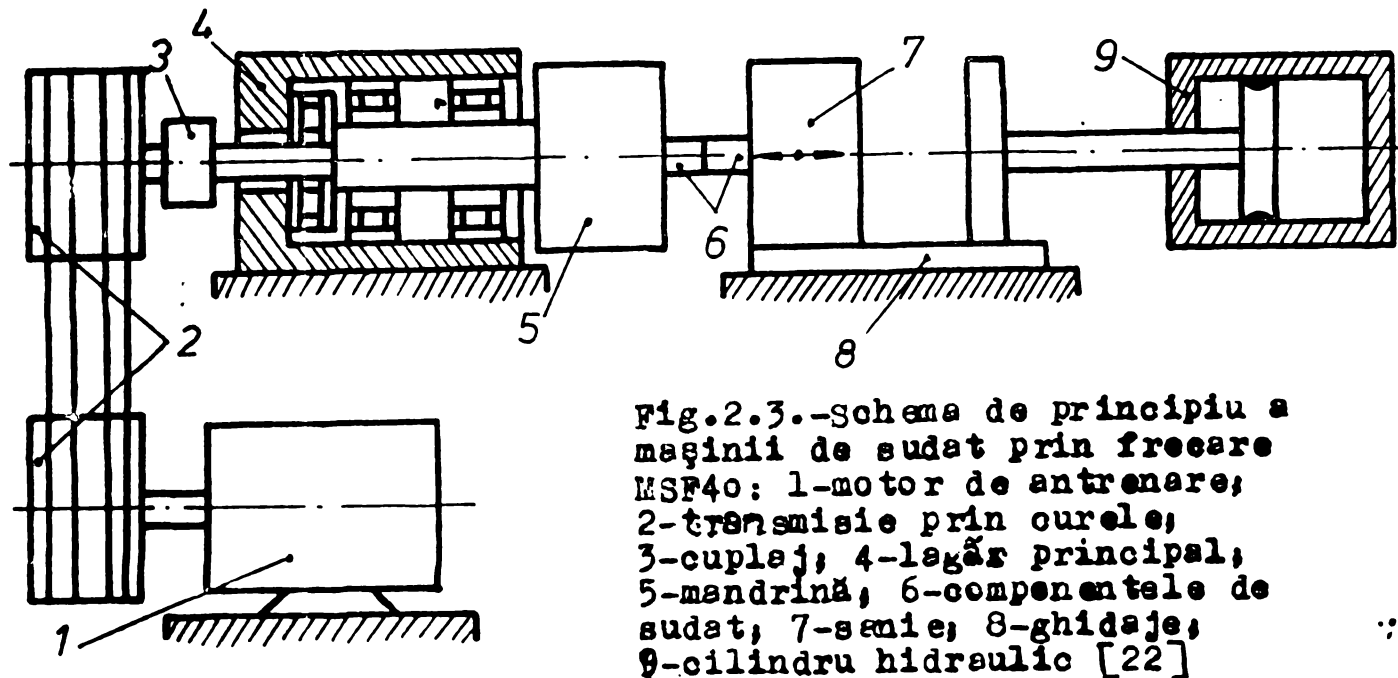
Schema de principiu a mașinii de sudat prin frecare MSF40: 1-motor de antrenare; 2-transmisie prin curele; 3-cuplaj; 4-legătură principală; 5-mandrină; 6-componentele de sudat; 7-sanie; 8-ghidaj; 9-cilindru hidraulic [22]
